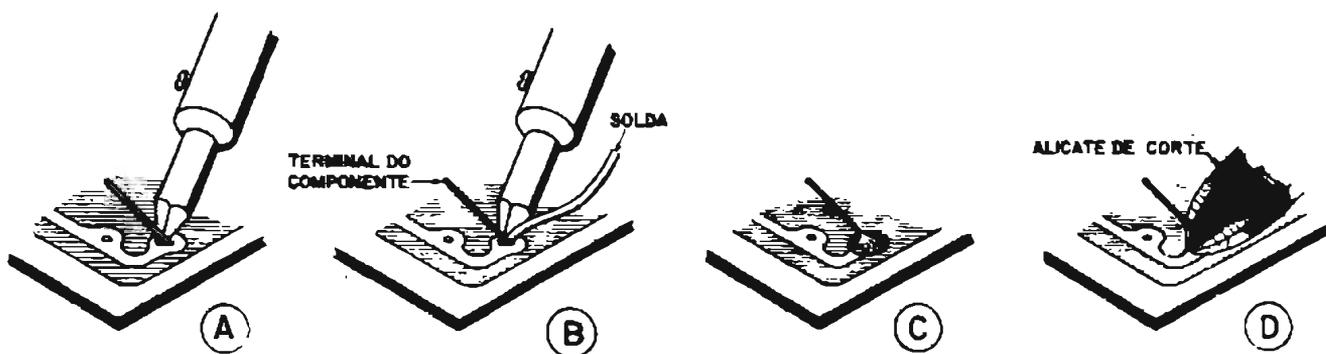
Diversas fases na soldagem de um componente à placa de fiação impressa
